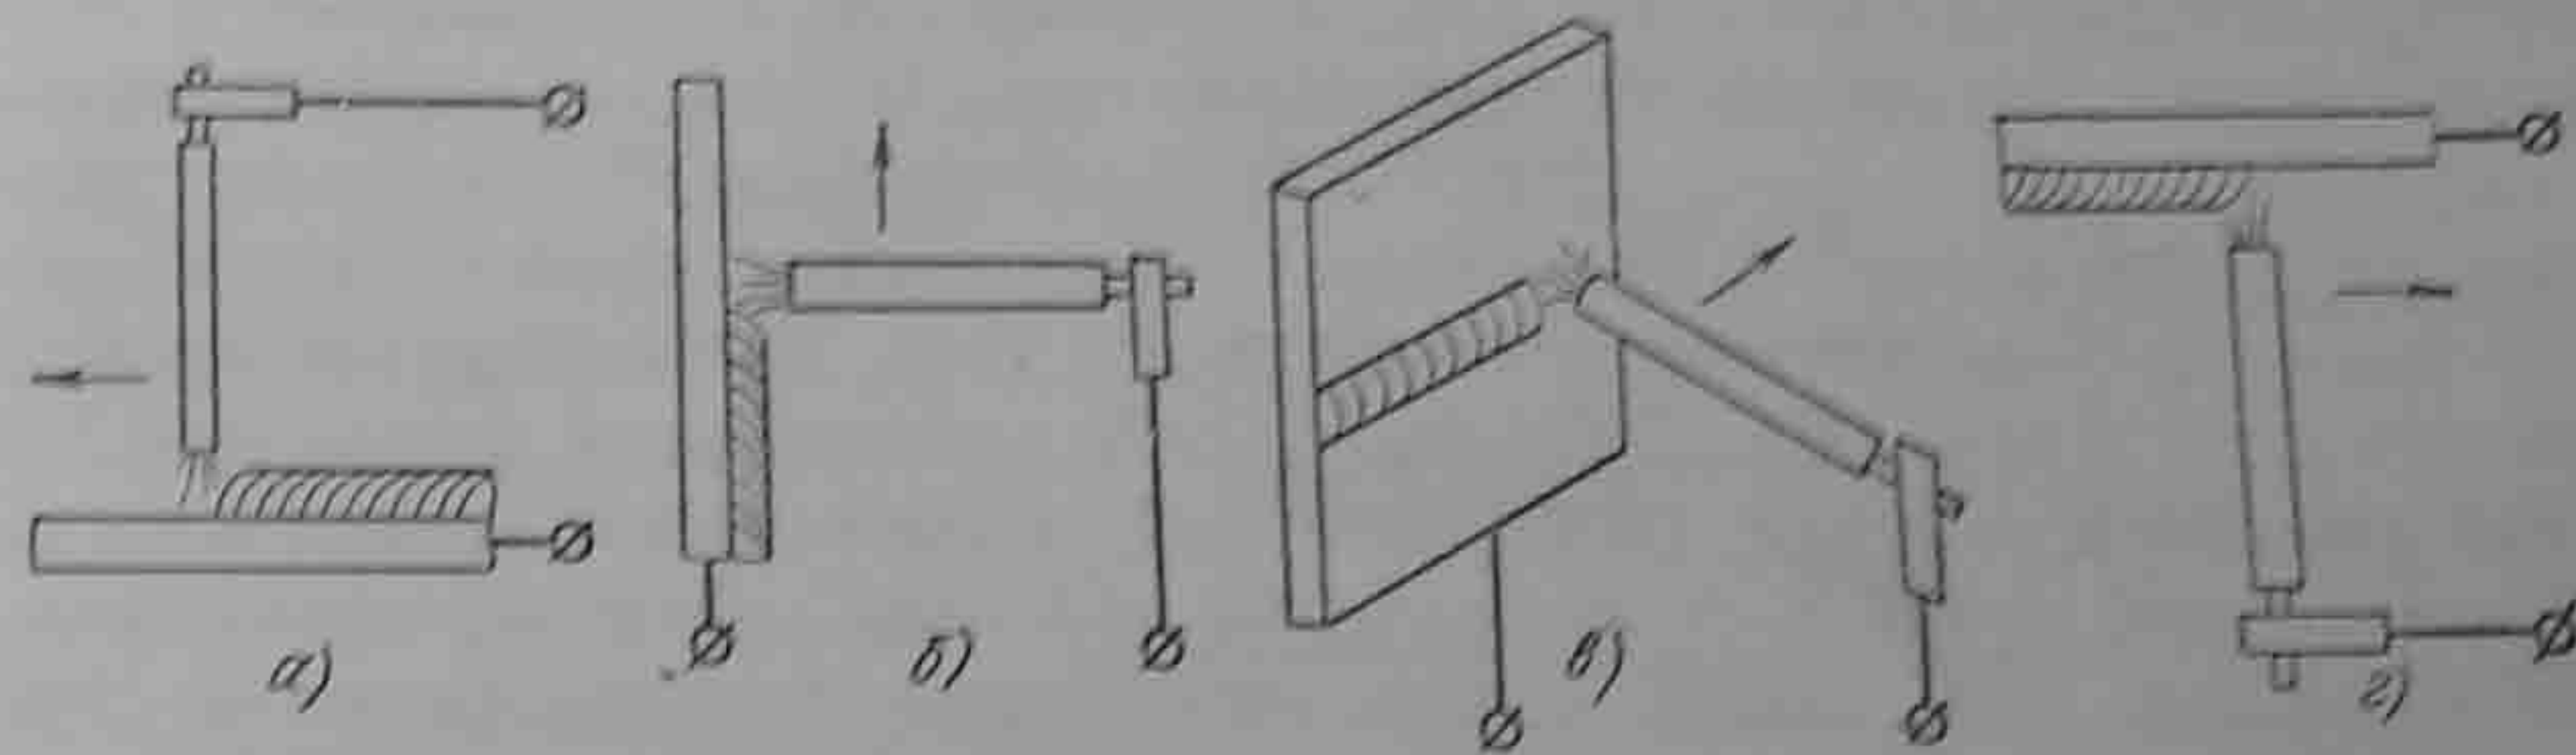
Возможные пространственные положения шва при ручной сварке: а — нижнее; б — вертикальное; в — горизонтальное; г — потолочное
